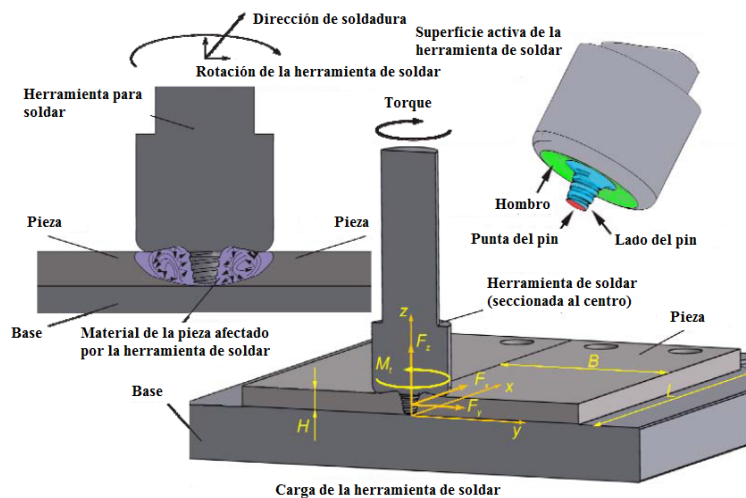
Soldadura por fricción agitación. Carga de la herramienta de soldar y superficies activas de la herramienta. Fuente: Miroslav *et al.* (2012).
